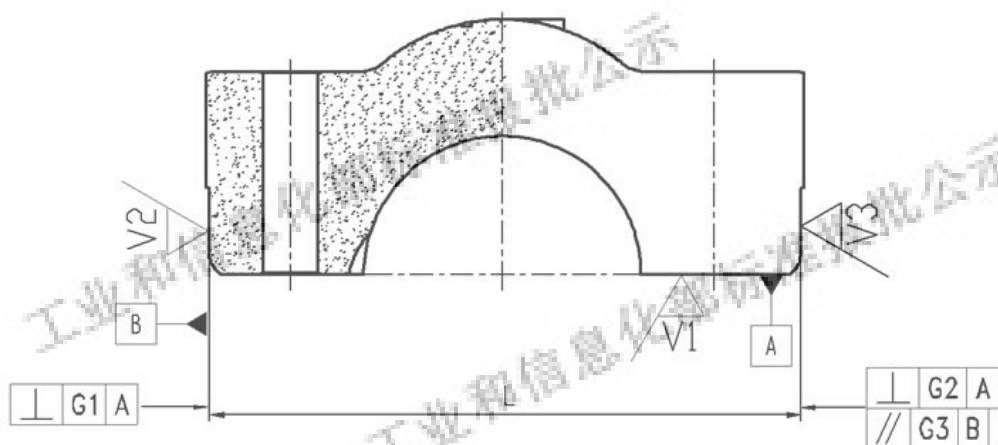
嵌配式曲轴轴承盖重要尺寸、几何公差及表面粗糙度标注示意图
